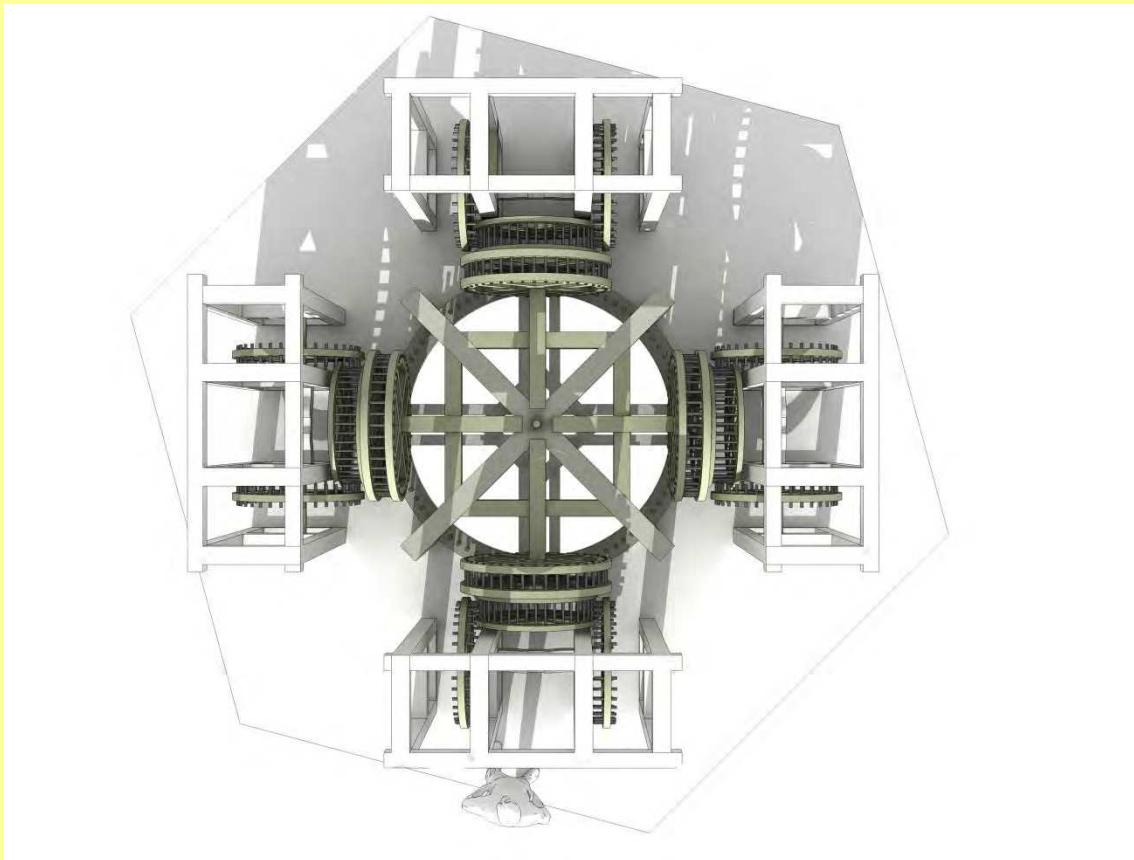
Reconstrucción hipotética de la máquina laminadora en la planta alta de la Casa de Moneda, vista de planta con escala humana (M. Borrero, Departamento de Restauración CNPAG).
